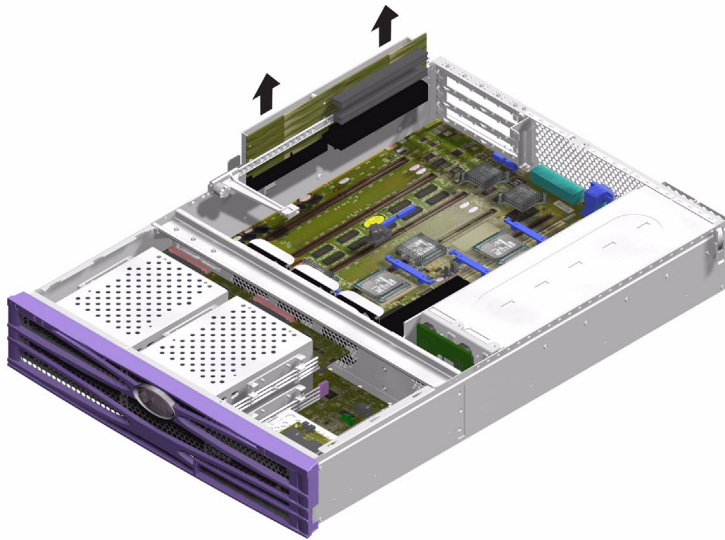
Rimozione del gruppo della PCI Riser Card
